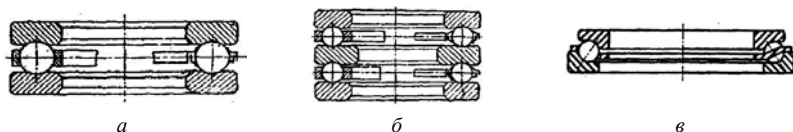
Шарикоподшипники упорные или упорно-радиальные типов:
